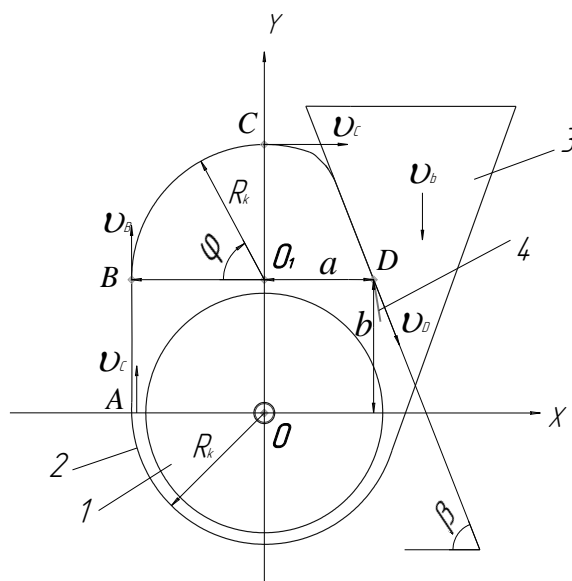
Схема визначення форми робочої поверхні кожуха дозатора - змішувача в зоні завантаження:
